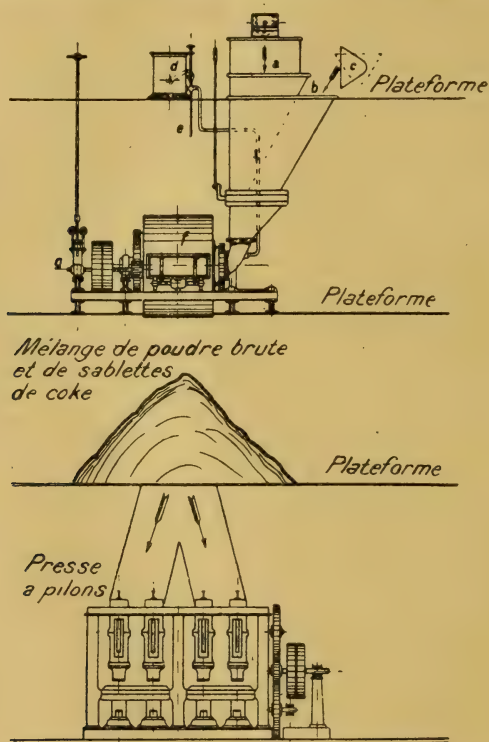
Vue d'ensemble de l'installation pour le mélange du combustible avec la poudre brute avant le briquetage
